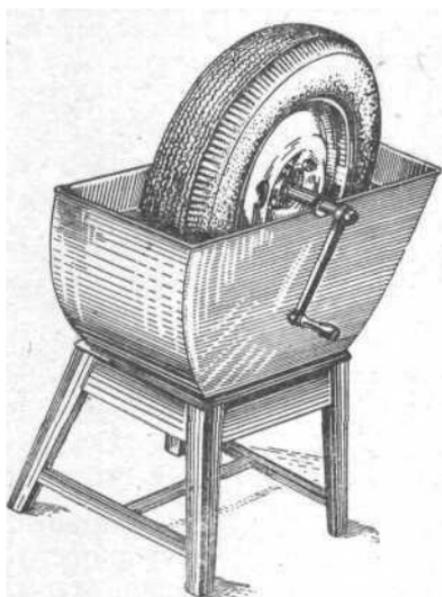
Ванна для проверки герметичности соединения обода колеса с диском
